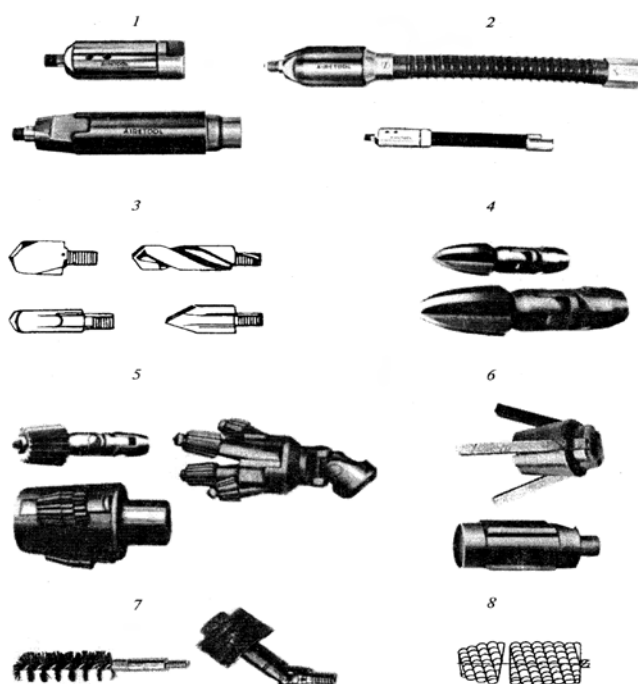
Пневмоприводы и рабочий инструмент для механической чистки труб:
